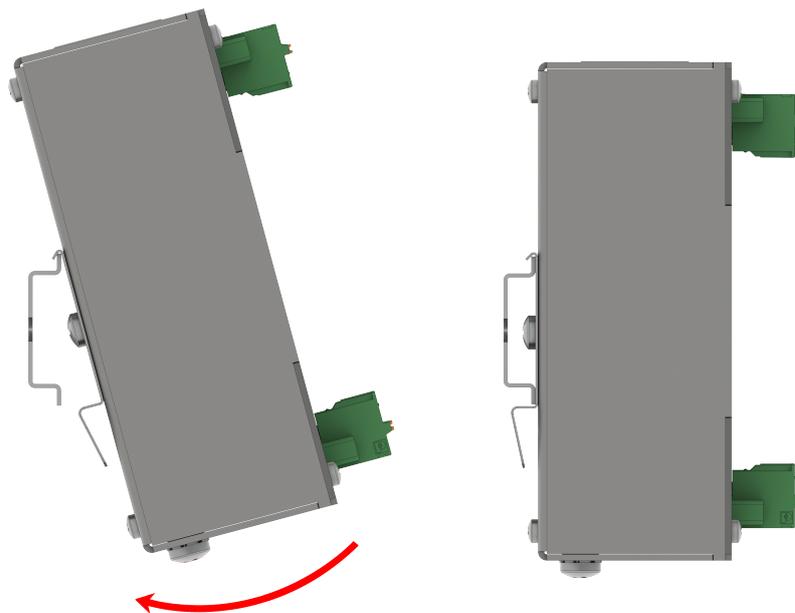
Монтаж устройства на DIN-рейку
